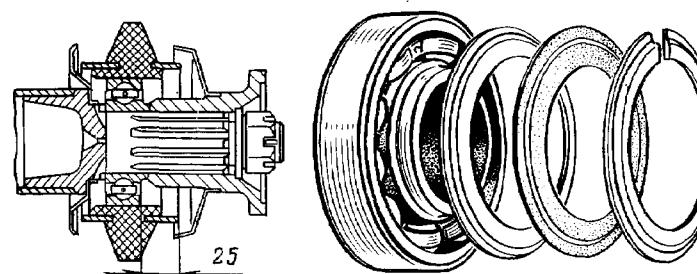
Сборка подшипника промежуточной опоры карданной передачи
